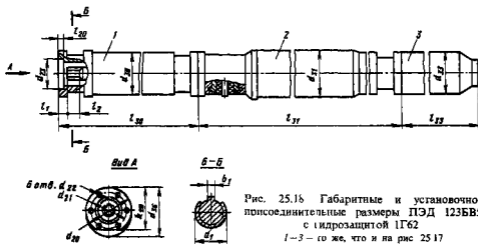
Габаритные и установочно-присоединительные размеры ПЭД 123БВ5 с гидрозашитой 1Г62
